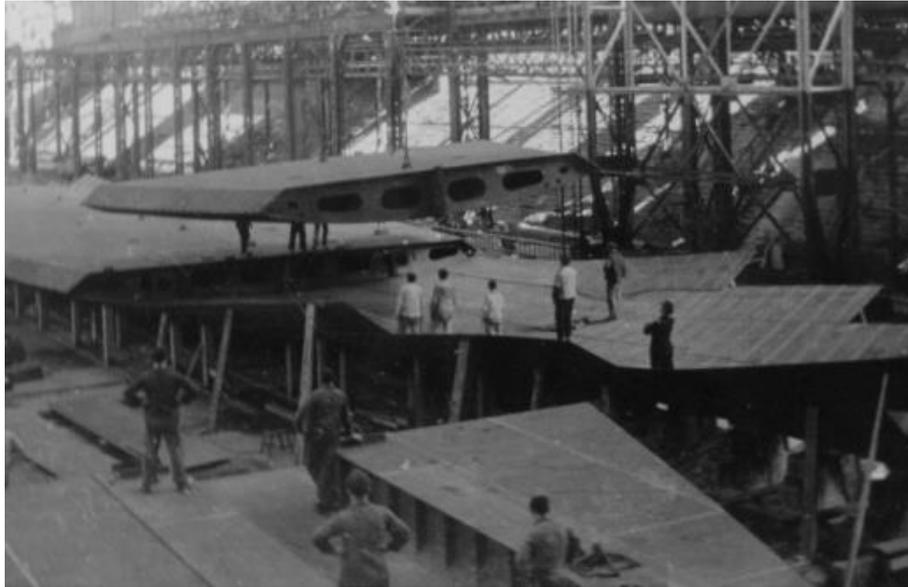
Mise en place d'un double fond sur le bordé de fond
